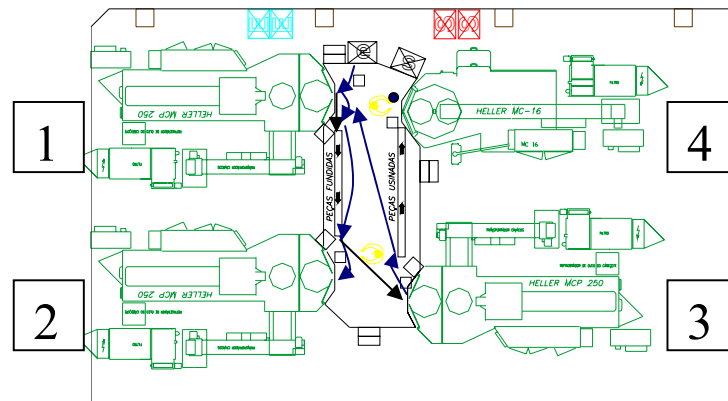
LAY OUT DA CÉLULA DE USINAGEM
